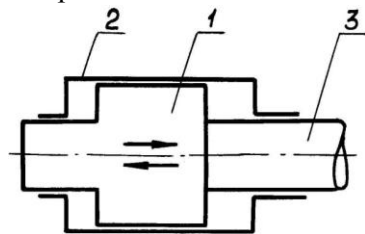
Принципова схема пневмоударника П1-75: 1 - поршень; 2 - корпус; 3 - передня головка
